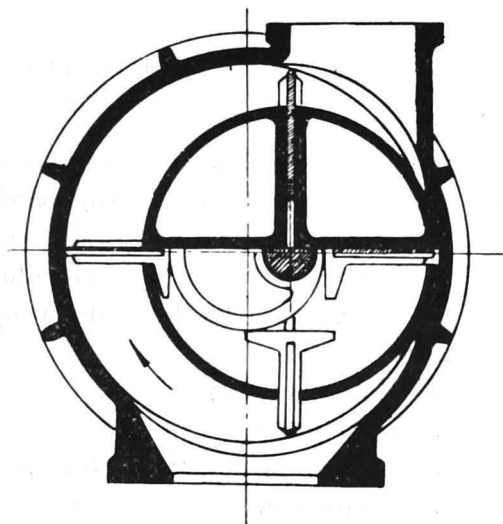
Compresorul cu piston și aripi tip Kromag-Zoller Z 9.
